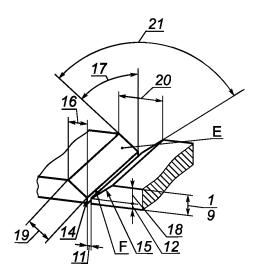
Подготовка под сварку стыкового соединения с V-образным скосом кромок и с притуплением
